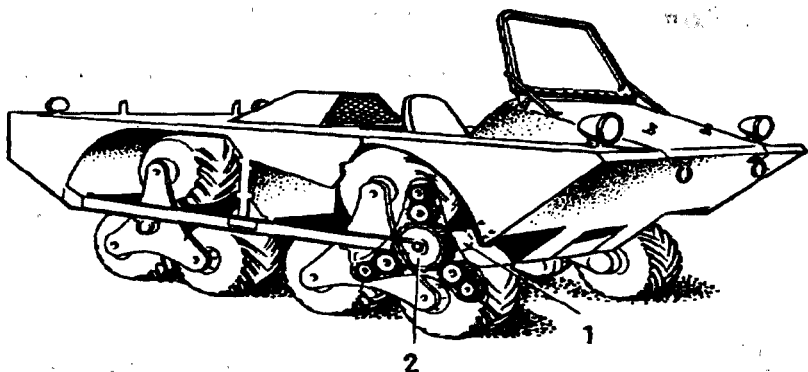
Колесно-шагающий движитель типа Пади-вагон:
